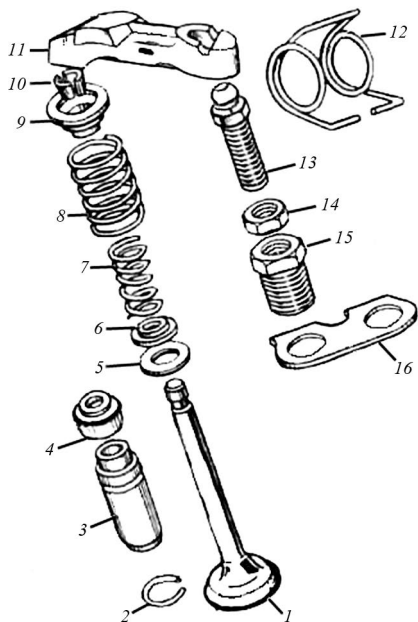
Детали клапанной группы и привода клапанов: 1 – клапан; 2 – стопорное кольцо направляющей втулки; 3 – направляющая втулка; 4 – сальник клапана; 5, 6 – опорные шайбы внутренней и внешней пружины; 7, 8 – внутренняя и внешняя возвратные пружины; 9 – тарелка пружины; 10 – сухари; 11 – рычаг привода клапана; 12 – пружина рычага; 13 – упорный винт; 14 – контргайка упорного винта; 15 – втулка упорного винта; 16 – стопорная пластина пружины рычага
